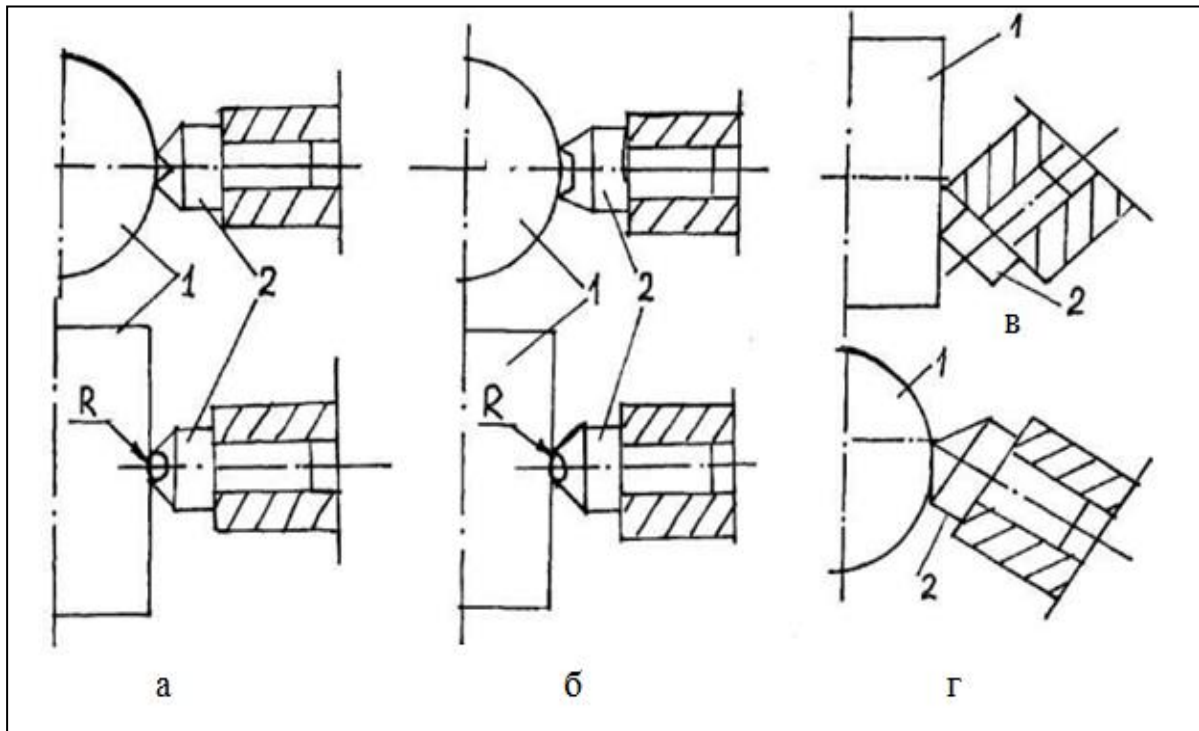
Схема установок випрасовувателів при обробці циліндричної поверхні: а - сферична форма заточування, б - циліндрична, в - тороїдальна, г - конічна; 1 - оброблювана поверхня, 2 – заточування
